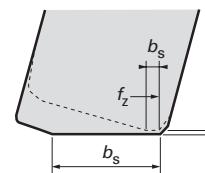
Utilisation d'une plaquette de planage munie d'un biseau plan surdimensionné, légèrement convexe
